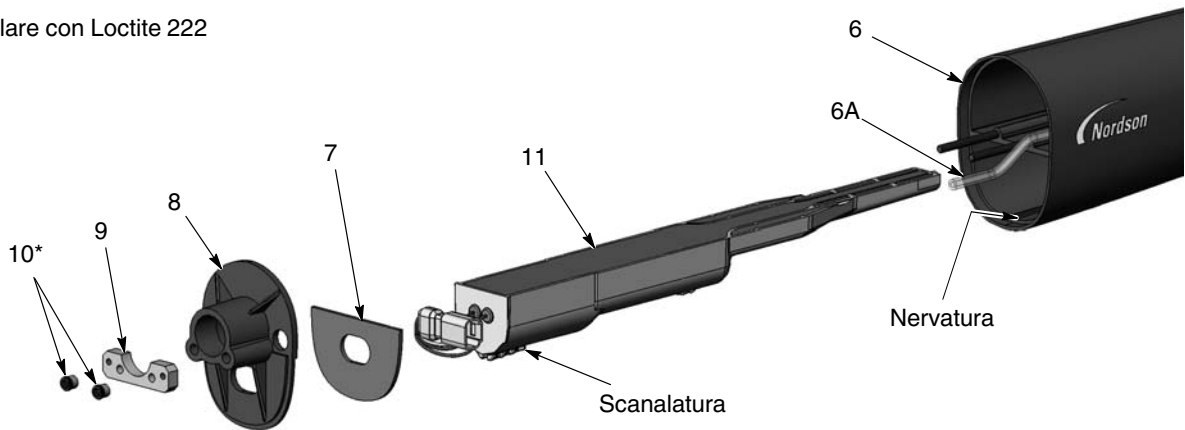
Smontaggio della pistola con montaggio su tubo 4 di 5
